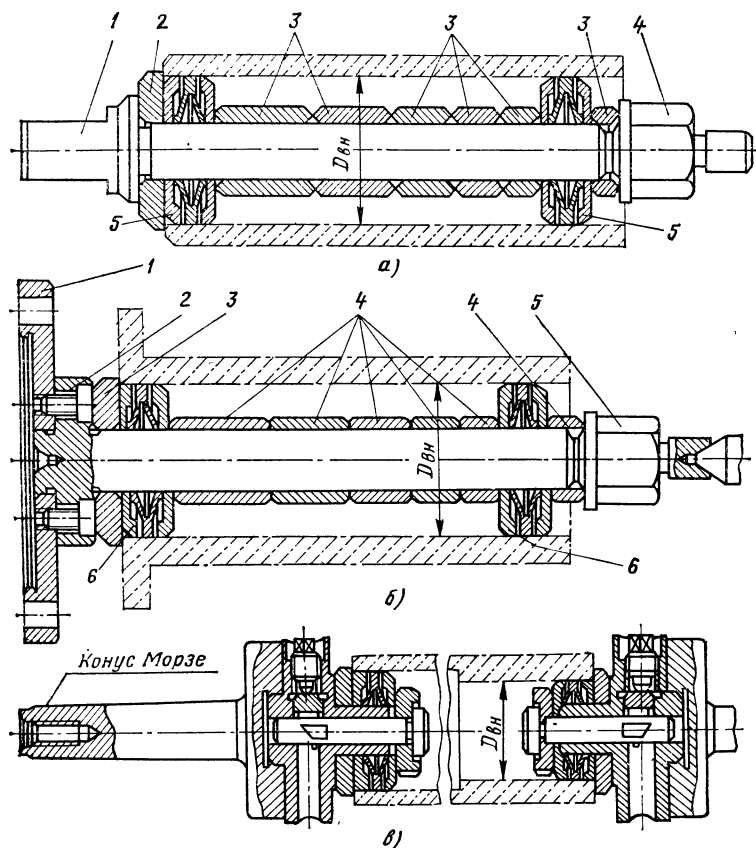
Оправки с упругими шайбами для закрепления деталей типа втулок
